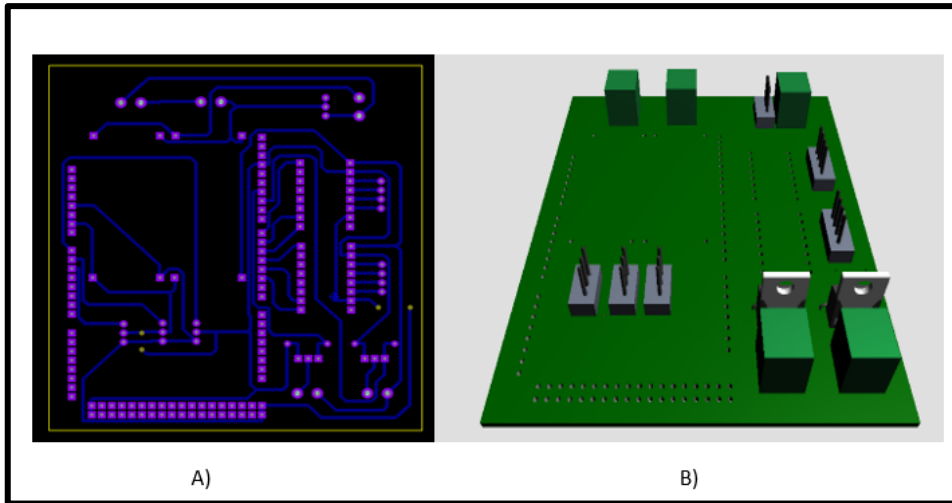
Placa PCB central de RAADUV, A) Vista inferior y B) Vista superior
